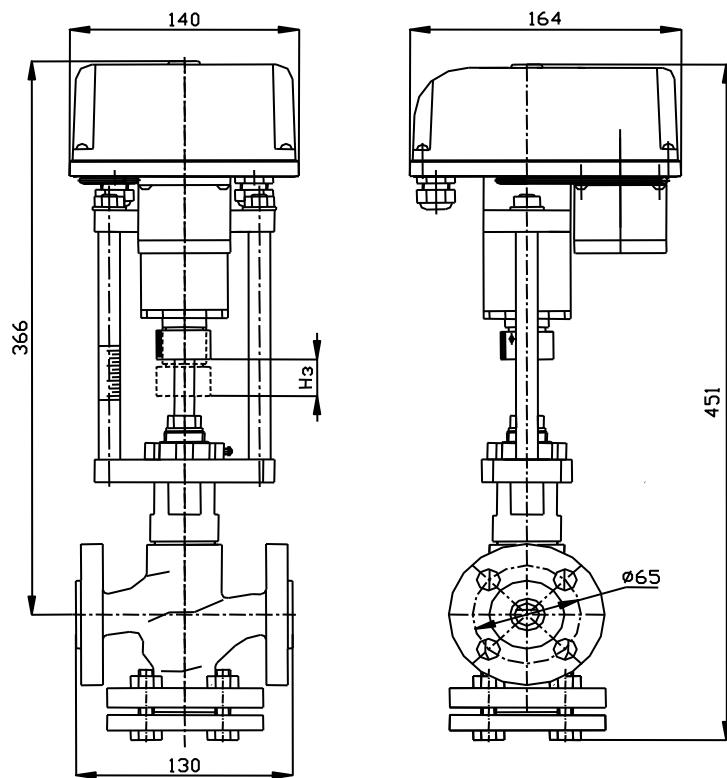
Габаритные, установочные и присоединительные размеры клапана.
